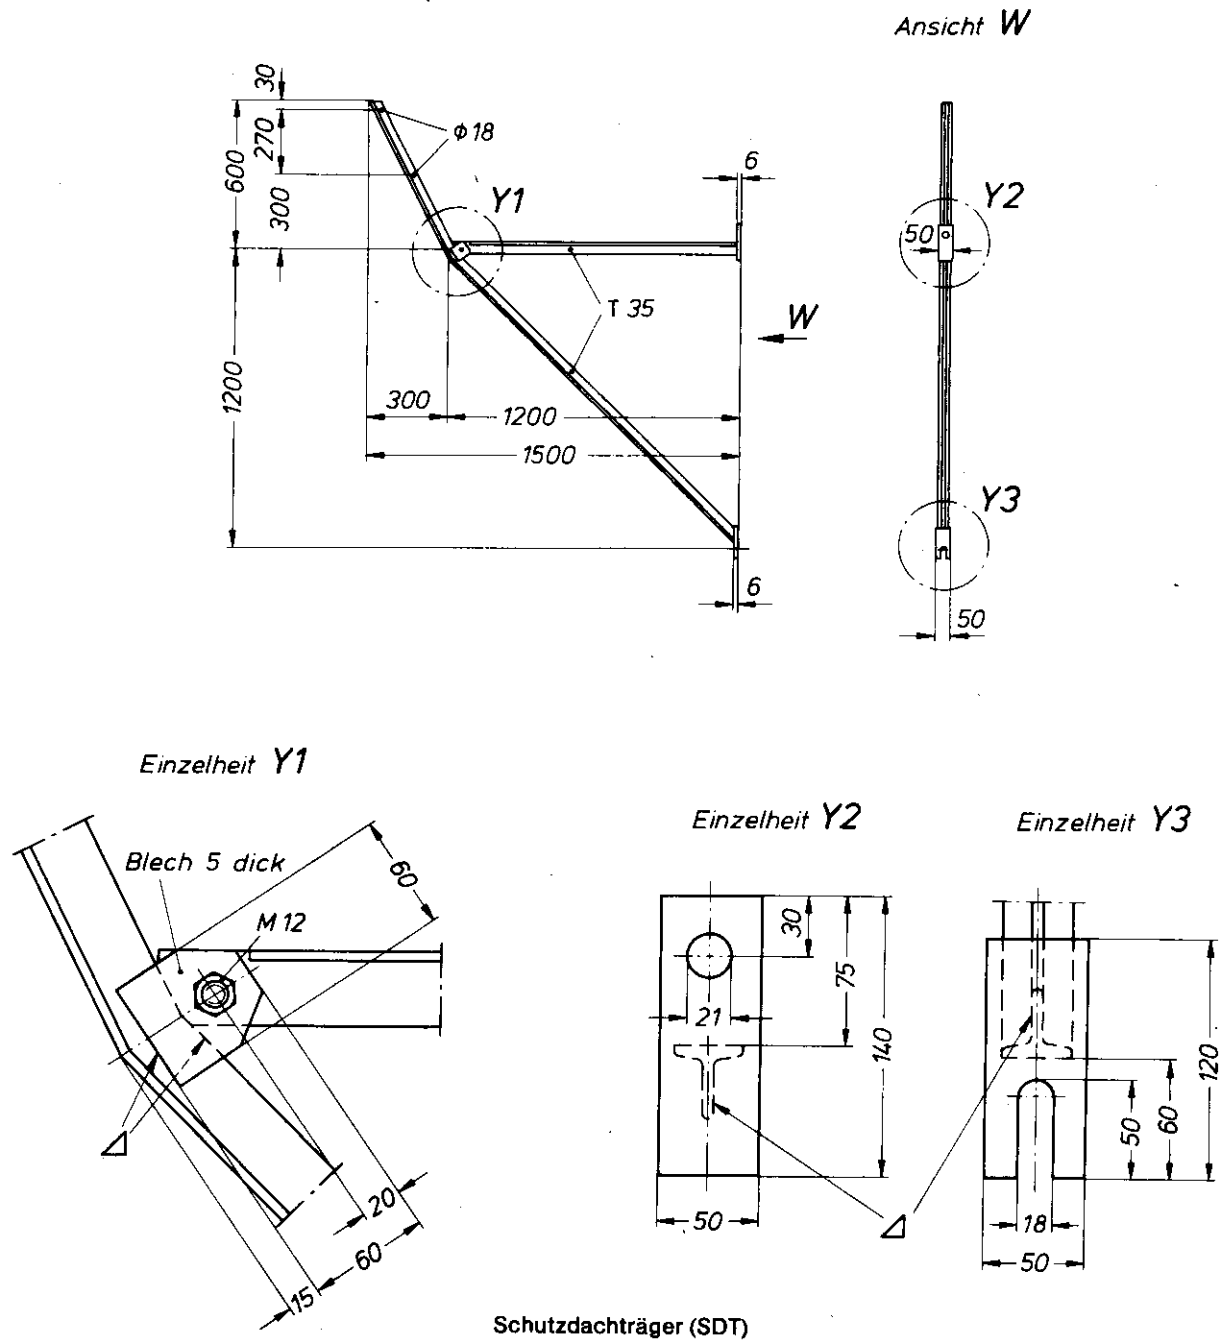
(Fortsetzung) Formen, Maße und Werkstoffe von Gerüstbauteilen aus Stahl nach Abschnitt 4.2.3 (Maße in mm)
